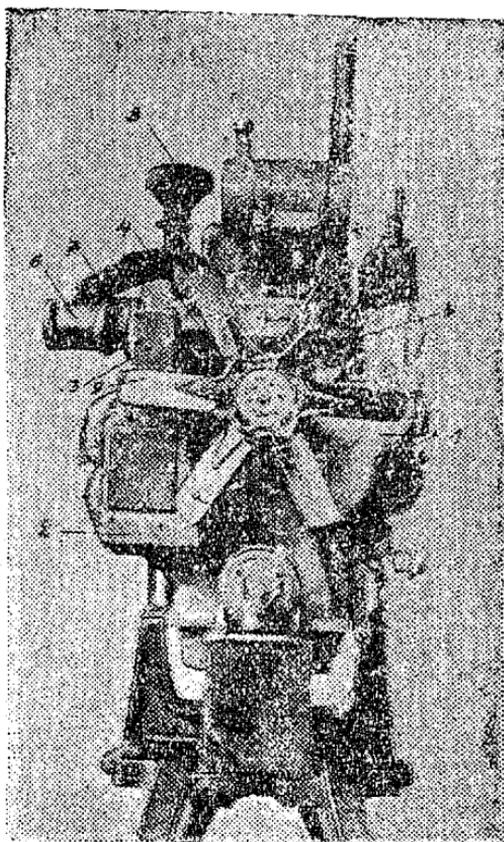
Общий вид газового двигателя МГ-17 спереди: 1—кожух шестерен распределения; 2—крышка регулятора; 3—корпус дроссельной заслонки; 4—патрубок отвода газа из корпуса дроссельной заслонки; 5—патрубок всасывающей трубы; 6—смеситель; 7—патрубок подвода воздуха к смесителю; 8—воздухоочиститель; 9—вентилятор.
